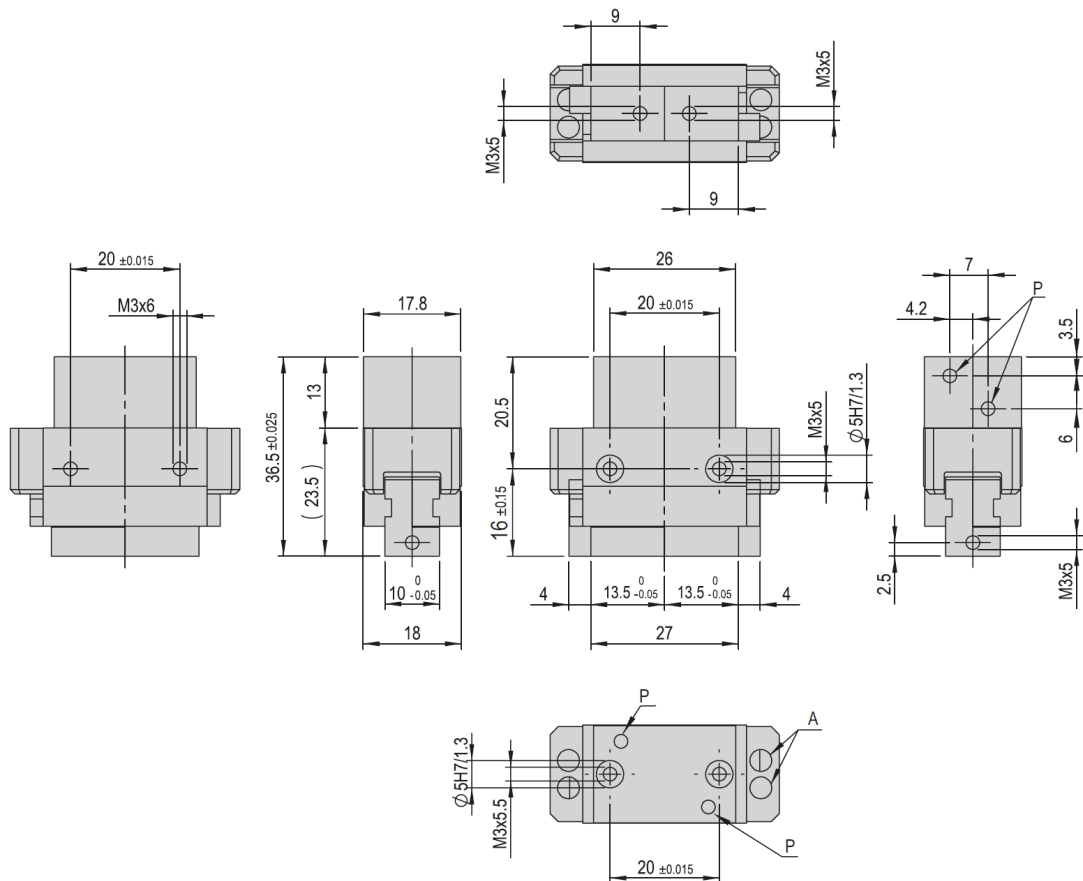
Masszeichnung Präzisionsgreifer PG 16 NN
